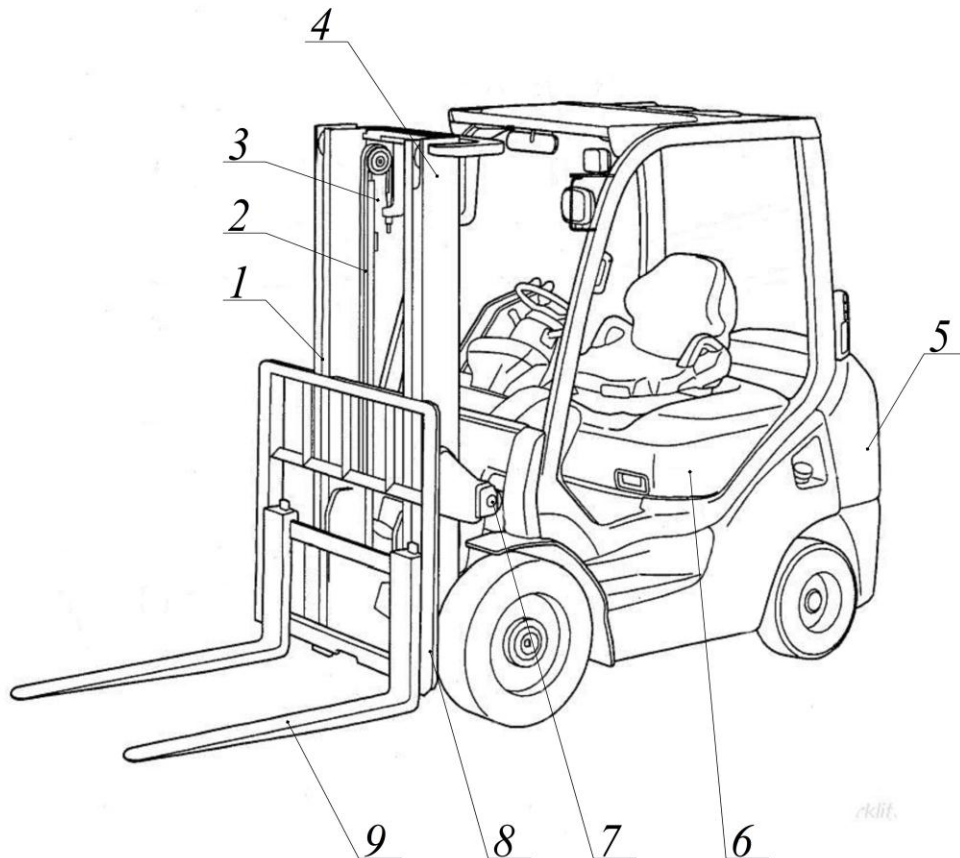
Загальний вигляд вилкового навантажувача: 1 – щогла; 2 – ланцюг; 3 – гідроциліндр підйому; 4 – нерухома рама; 5 – противаги; 6 – капот двигуна; 7 – гідроциліндр нахилу; 8 – каретка; 9 – вилка
